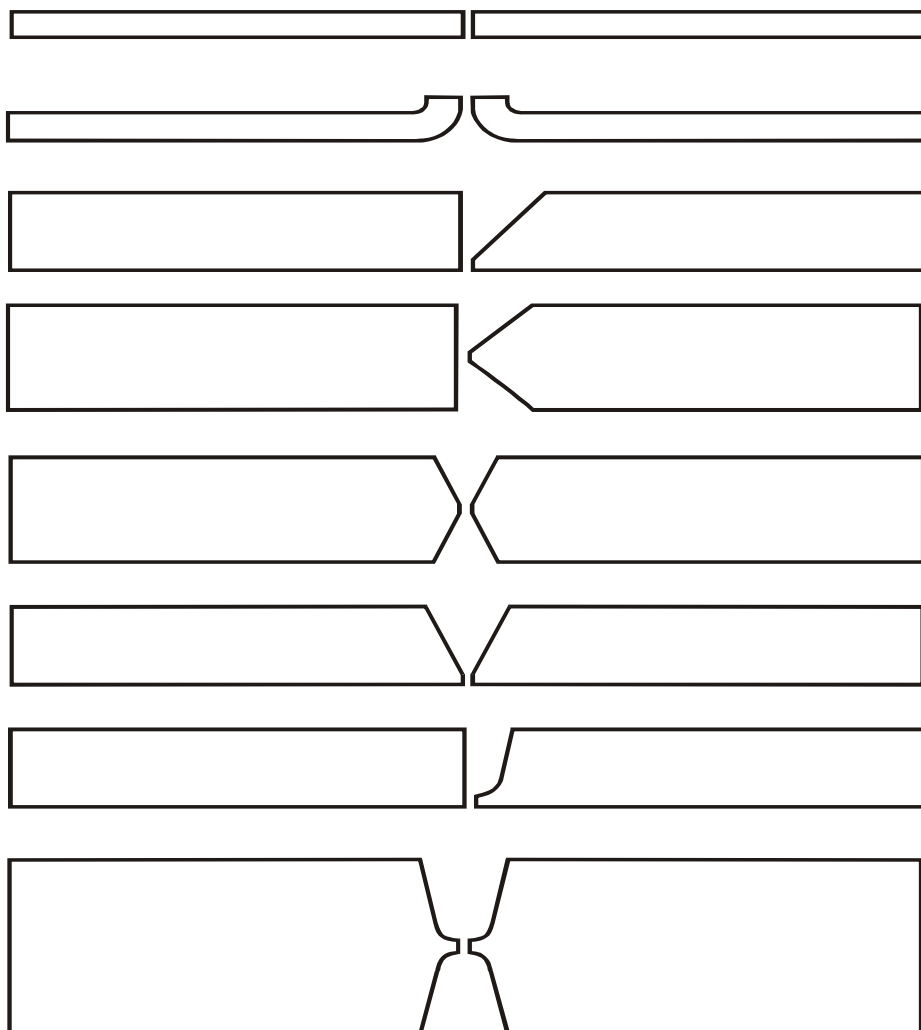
Формы подготовки свариваемых кромок стыковых соединений
